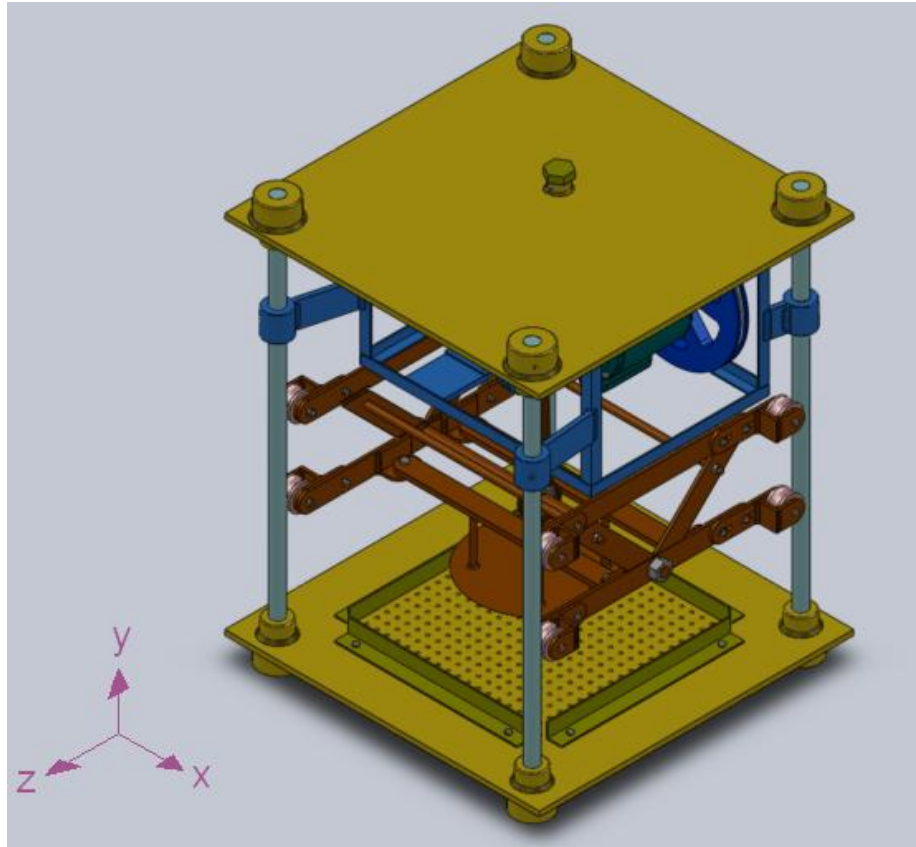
Equipo de ensayo ensamblado (vista isométrica).
